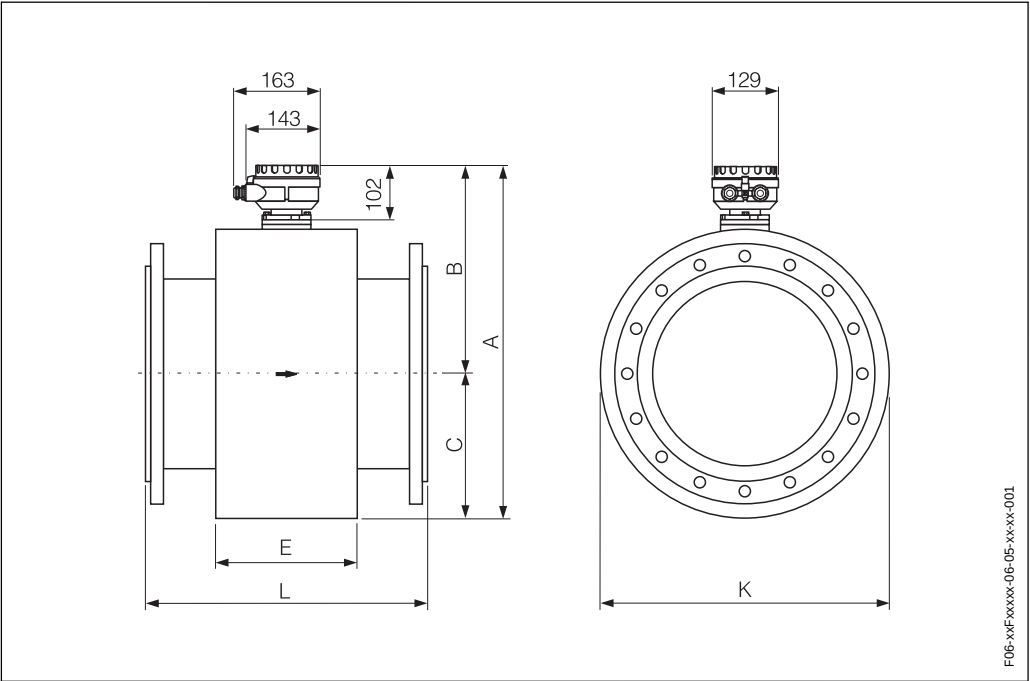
Dimensões do Promag P / DN ≥ 350 (versão remota)
